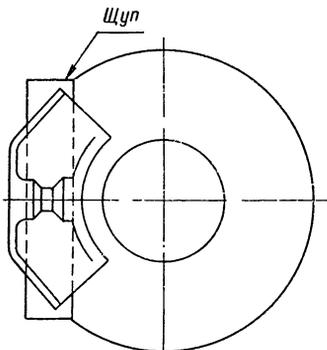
Схема установки щупа при регулировке зазора между диском и колодками ручного тормоза
